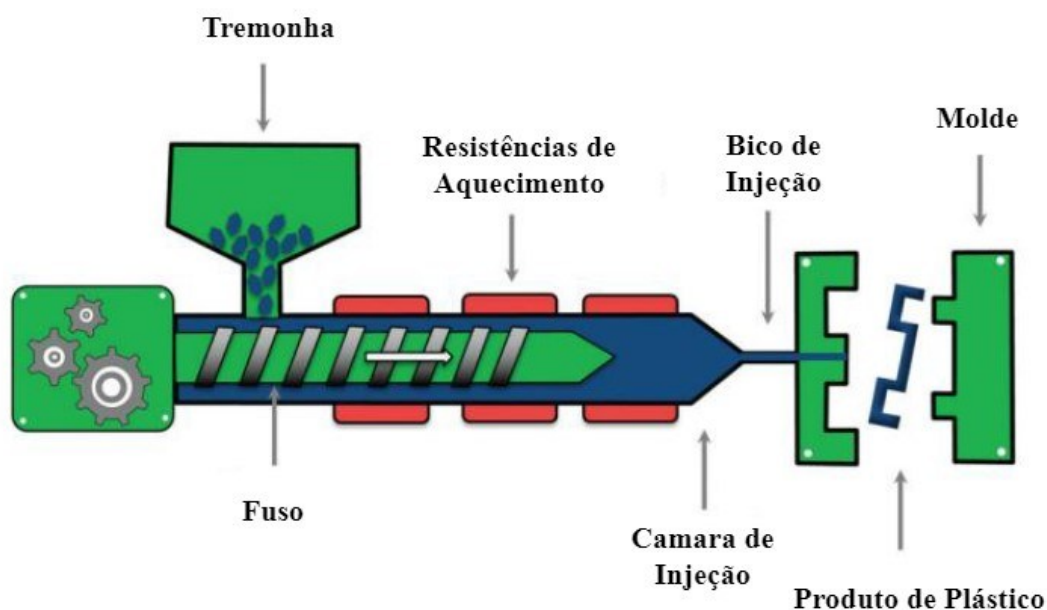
Componentes principais de uma máquina de injeção (Adaptado de Frumosu et al., 2020)
